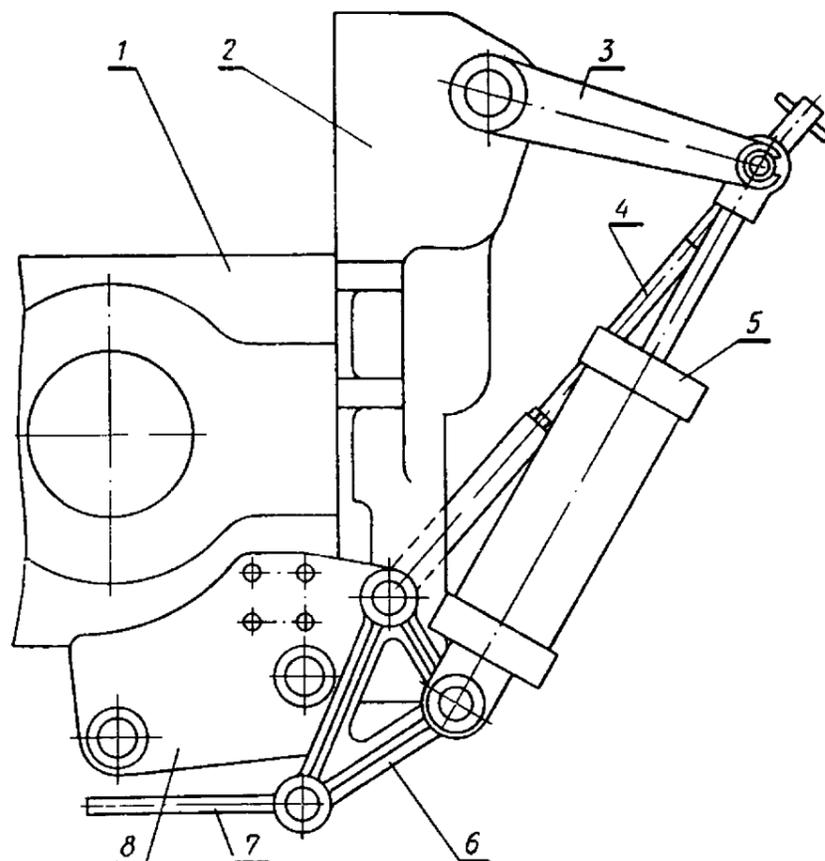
Схема перестановки гидромеханизма трактора для привода подъемного механизма косилки:
